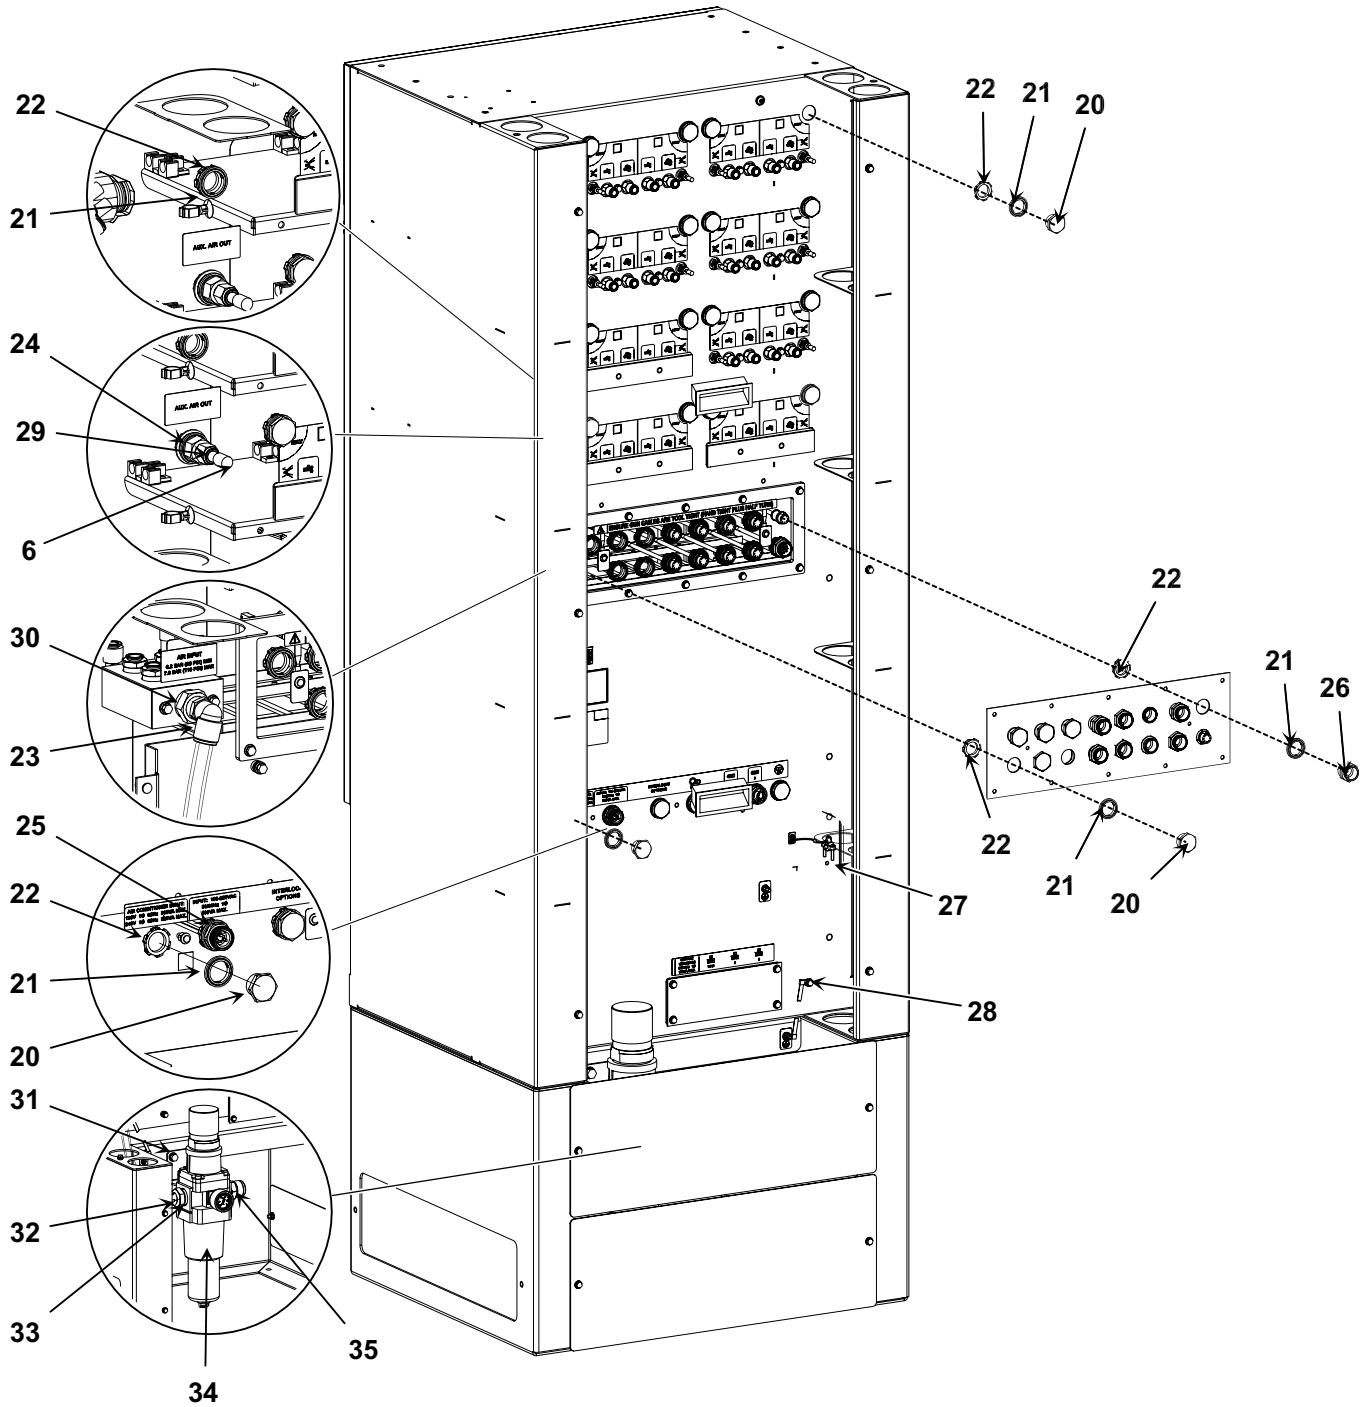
Componenten hulpregelaar 1 van 2
